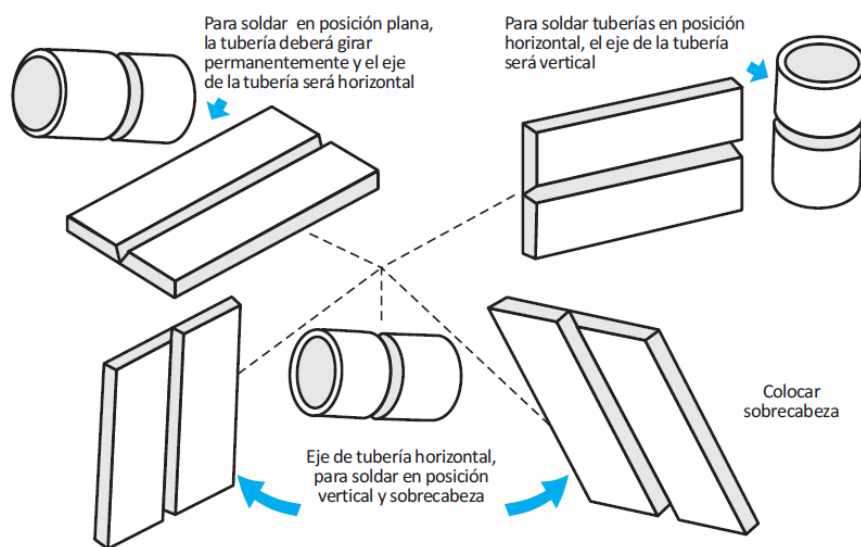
Diversas juntas y posiciones de soldadura.
